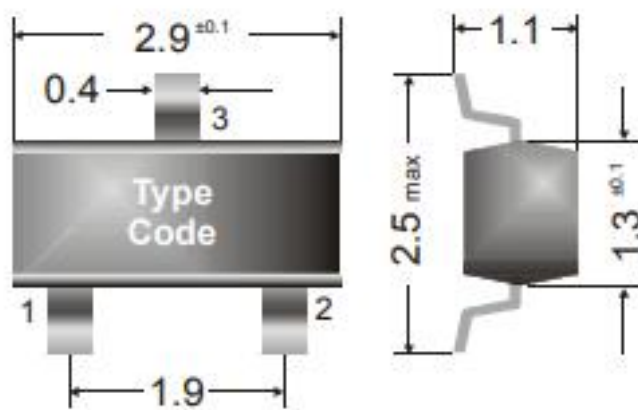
Габаритні розміри транзистора 2N7002
